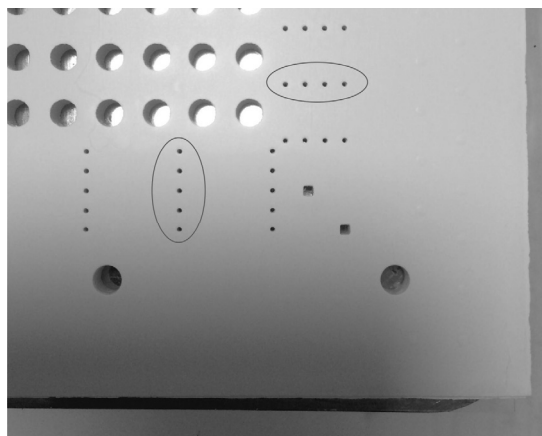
Пример отображения реперных меток для установки резки на заготовки CM-15
